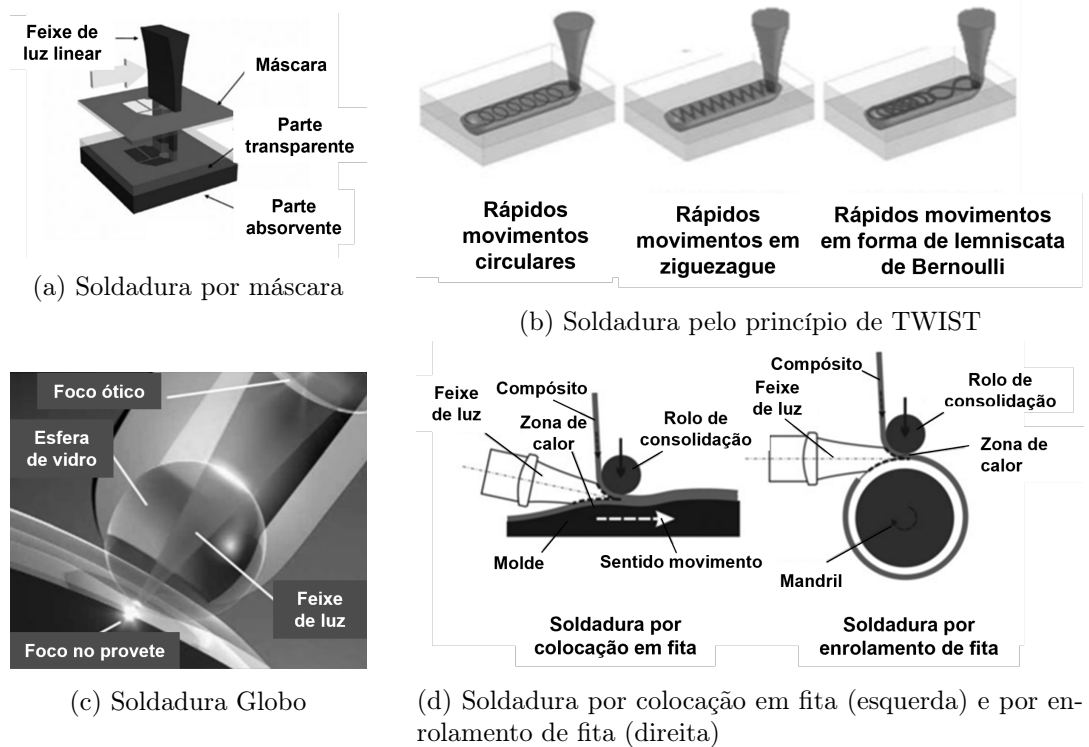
Outros processos de soldadura laser. Adaptado de [13].
